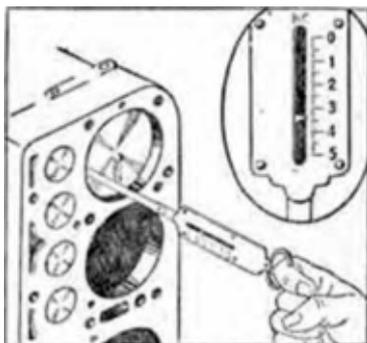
Проверка зазора в соединении поршень- цилиндр с помощью ленты-щупа и безмена.
